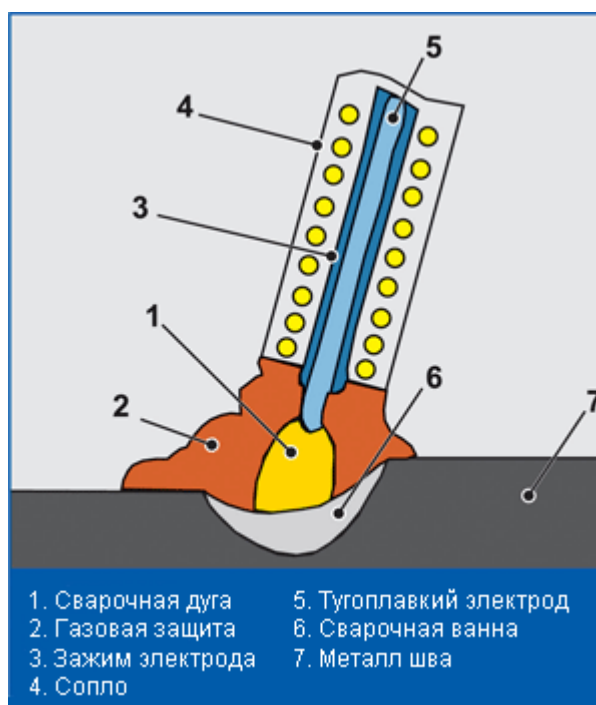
Ручная сварка неплавящимися вольфрамовыми электродами в среде защитного газа - аргона
